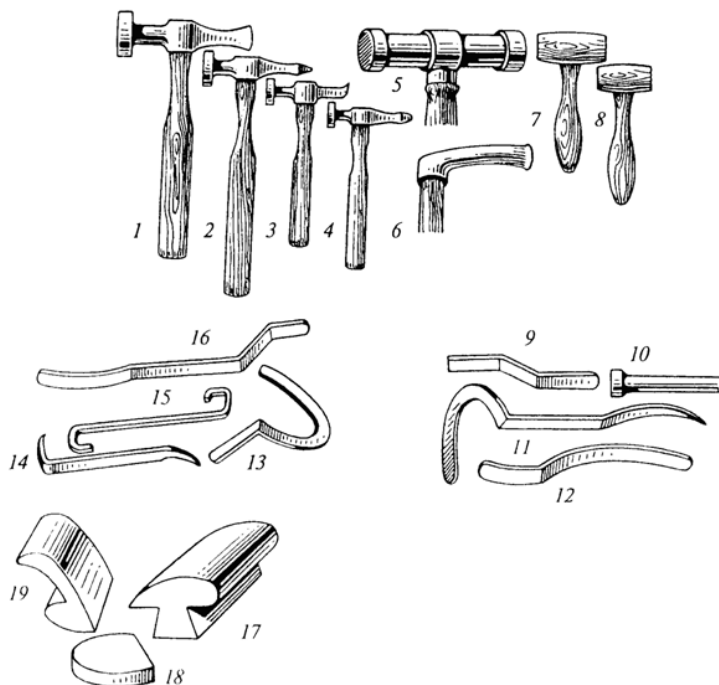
Комплект инструментов и приспособлений для правки и рихтовки кузовов:
